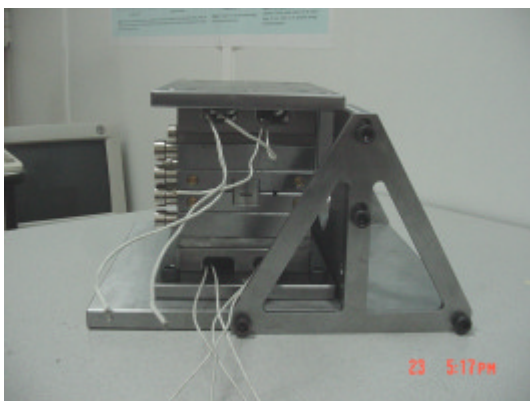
Fotografia do conjunto molde-estrutura interface montado
